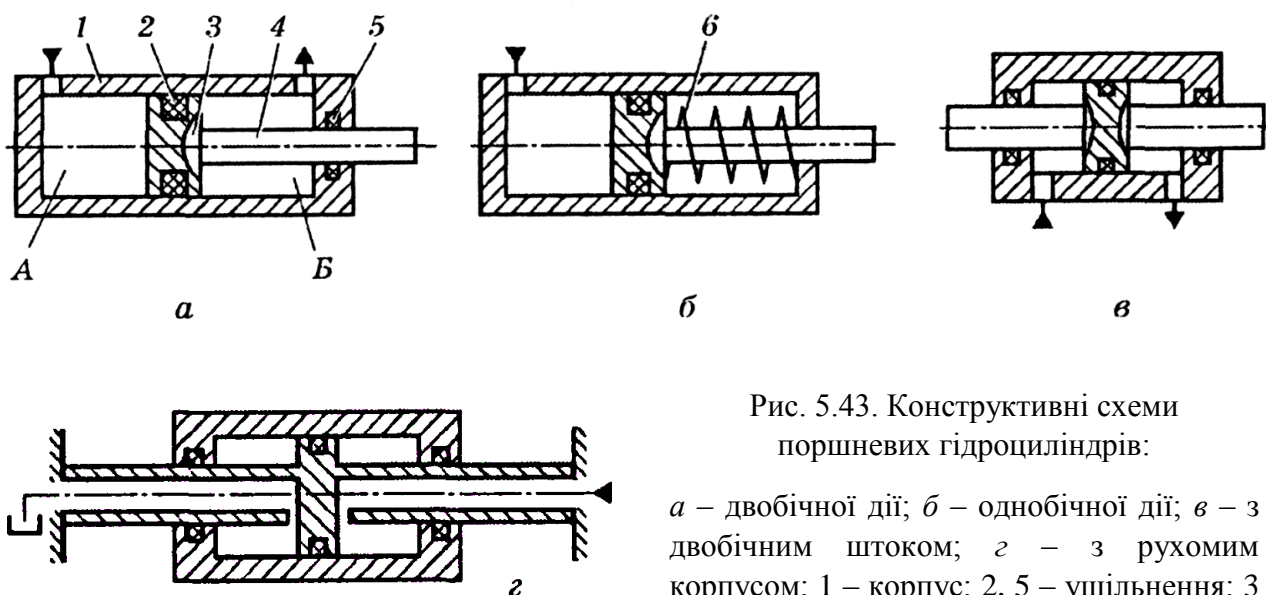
Конструктивні схеми поршневих гідроциліндрів:
